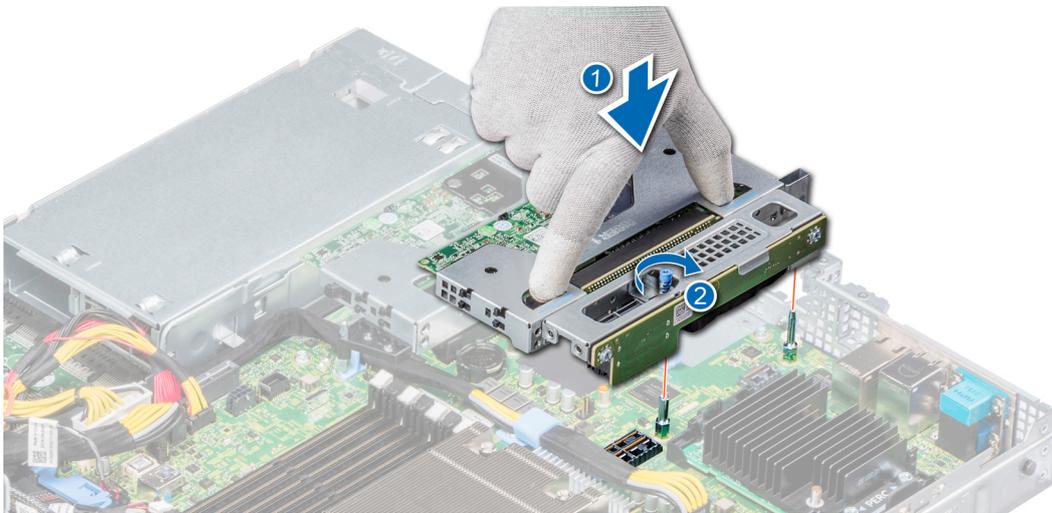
Instalación del soporte vertical de bajo perfil derecho
